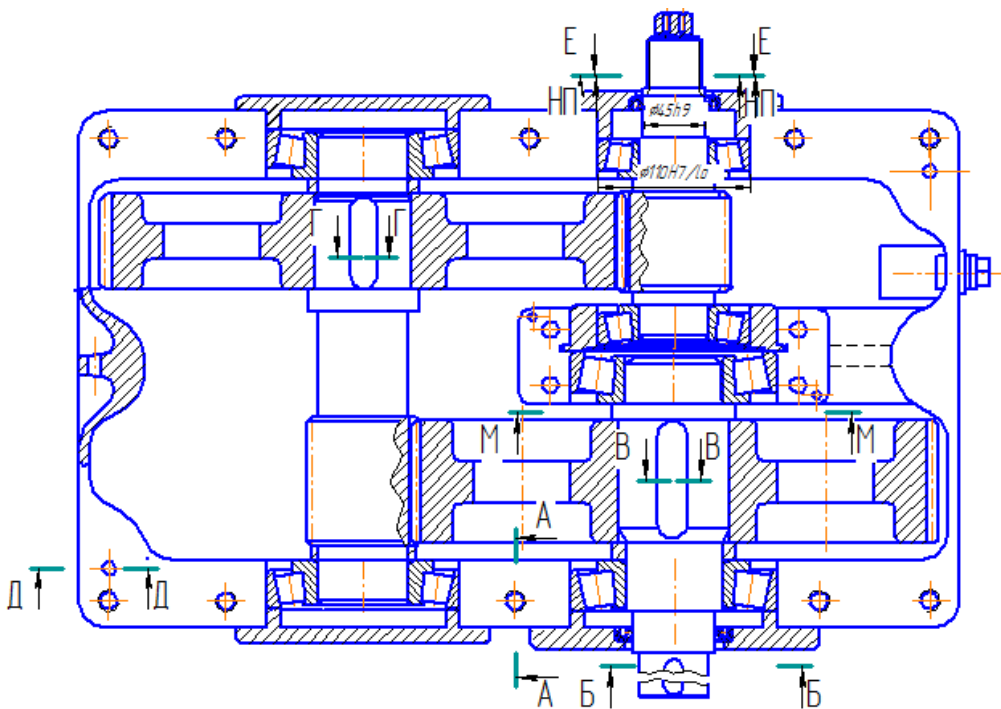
Поворотний редуктор зернозбирального комбайна
